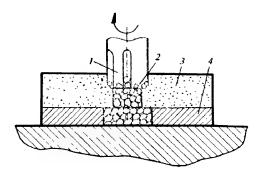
Схема обработки посадочного отверстия круга с использованием чугунного зерна:
